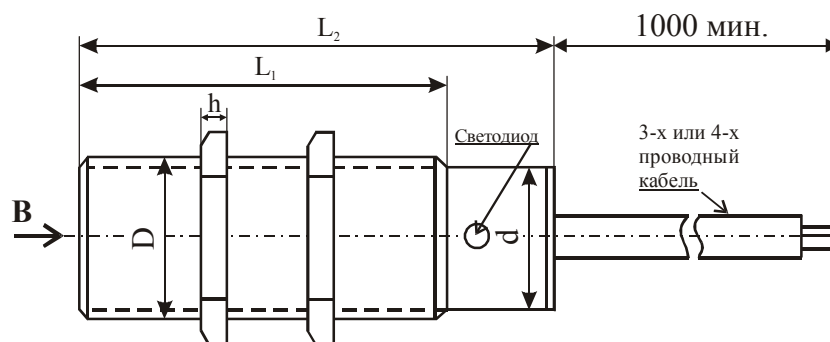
Внешний вид и габаритные размеры датчиков типа MRS-300, MRS-350
